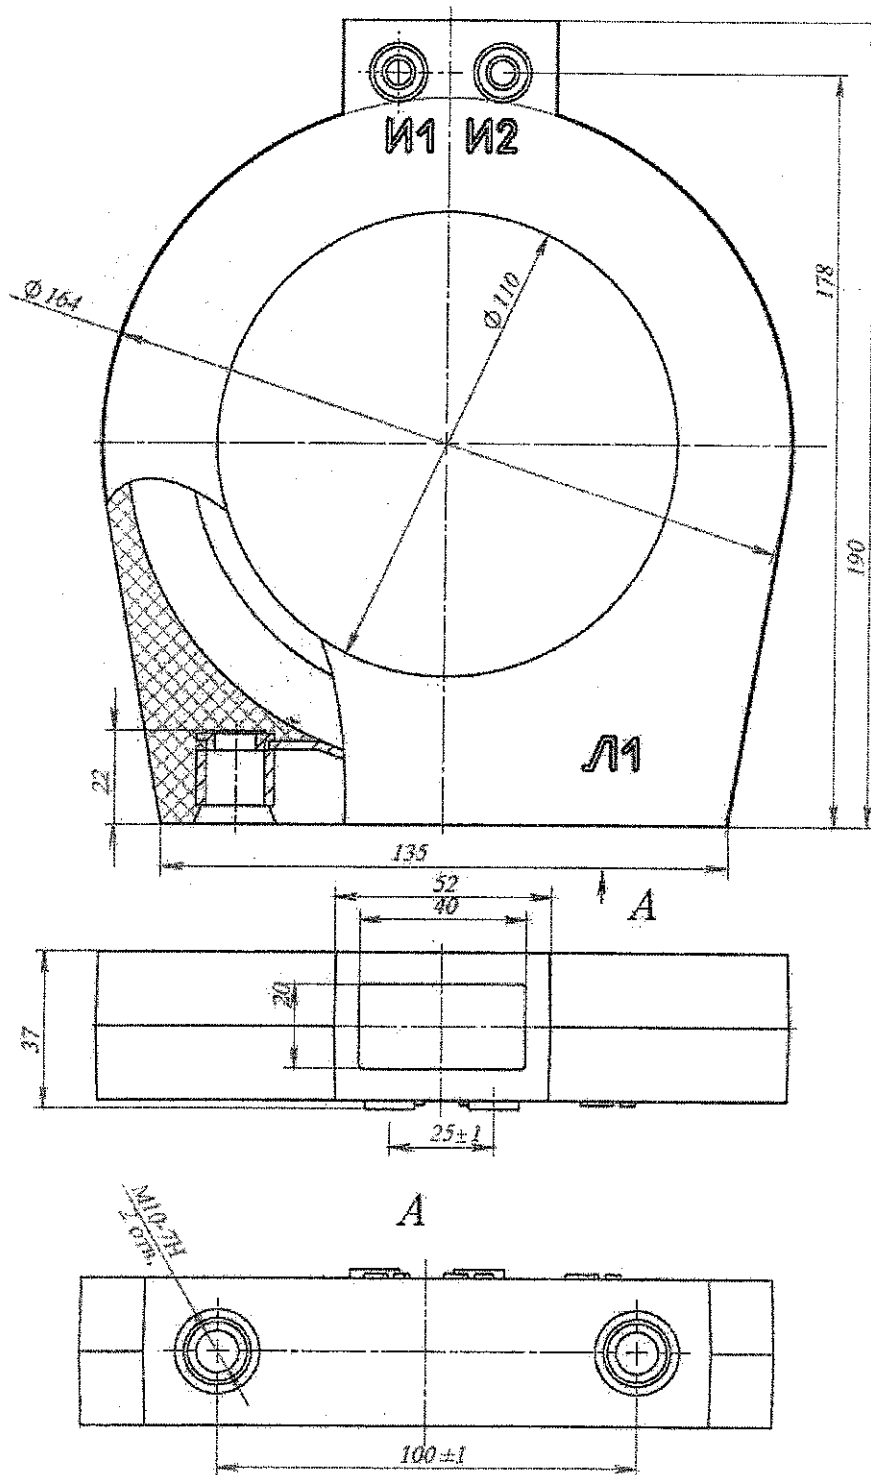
Общий вид и габаритные размеры трансформатора тока
